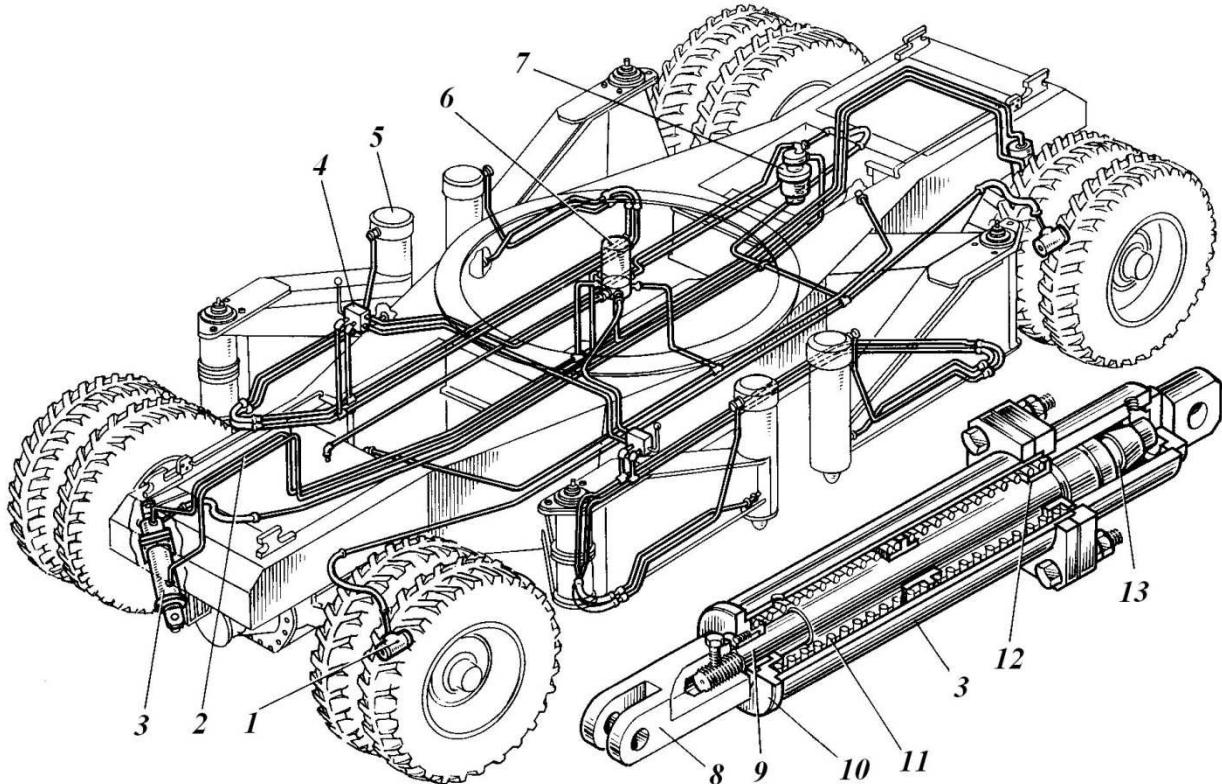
Схема размещения гидрооборудования на шасси пневмоколесного крана: 1 – тормозной гидроцилиндр, 2 – трубопровод, 3 – гидроцилиндр поворота колес, 4 – гидрораспределитель, 5 – гидроцилиндр выносной опоры, 6 – гидрошарнир, 7 – насос, 8 – проушина, 9 – шток, 10 – крышка, 11 – пружина, 12 – грязесъёмник, 13 – уплотнение
